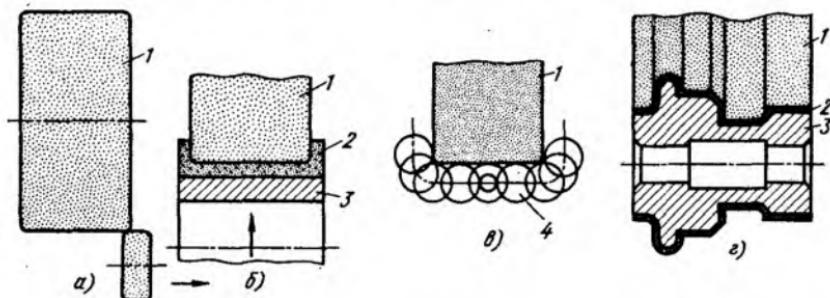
Схемы правки шлифовальных кругов алмазными роликами:
